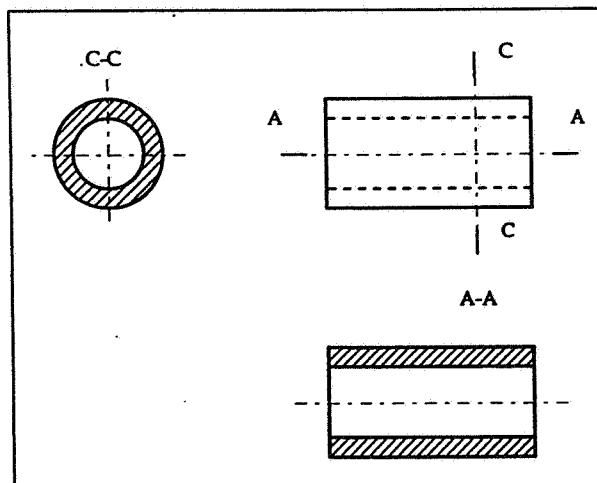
Sezione longitudinale A-A e trasversale C-C di un elemento tubolare.
